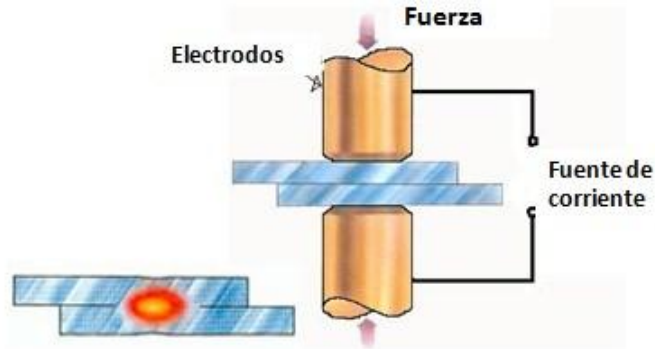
ELEMENTOS DE SOLDADURA FUERTE
